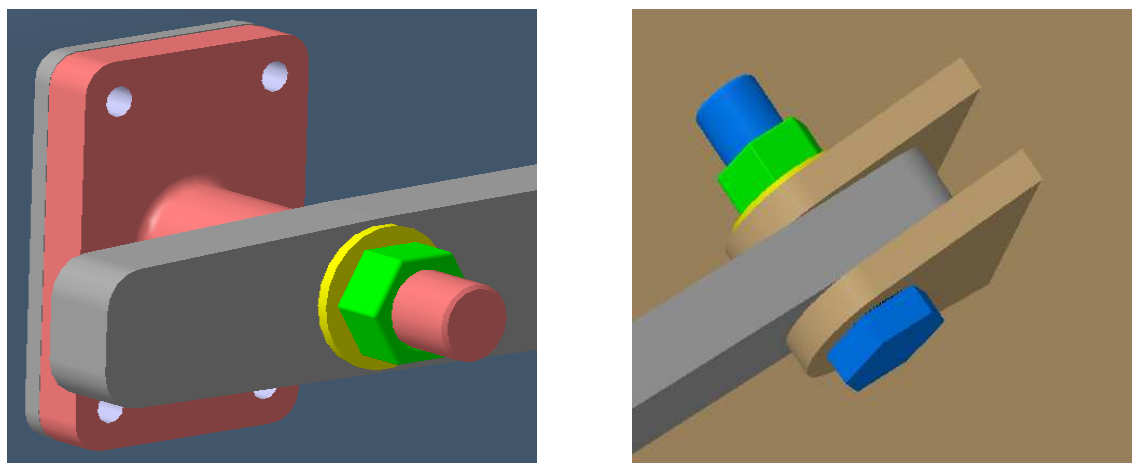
Příruba pro upevnění závěsných čepů motorového lože [9]
